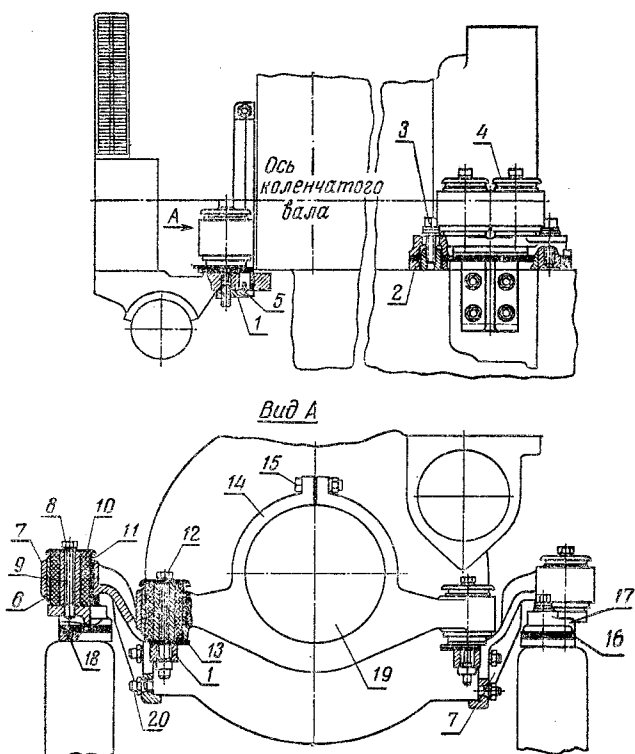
Крепление двигателя АМ-41 к раме трактора:
